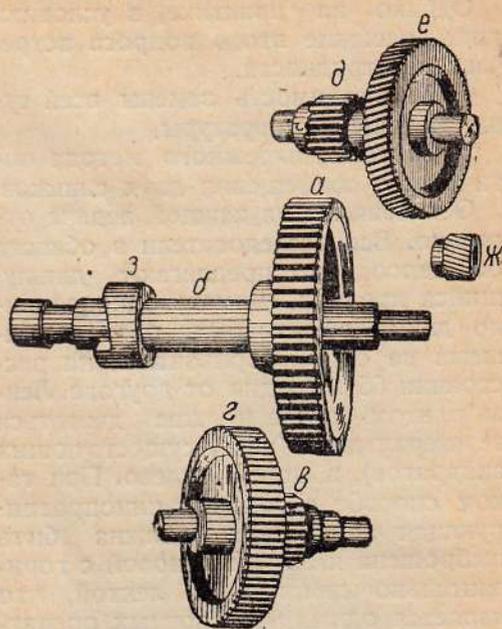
Детали механической части динамопривода ГОЗ, а — главная шестерня; б — главная ось; в — вторая промежуточная шестерня; г — третья промежуточная шестерня; д — четвертая промежуточная шестерня; е — пятая промежуточная шестерня; ж — рабочая шестерня оси якоря; з — храповая шайба для сцепления ручки привода с главной осью
